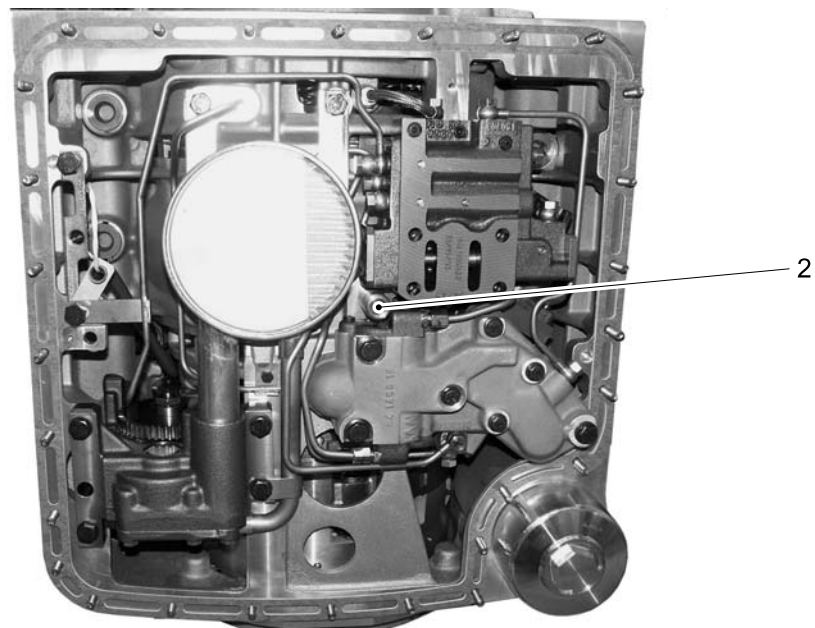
2 - Ablassschraube für das Öl im Wandler
